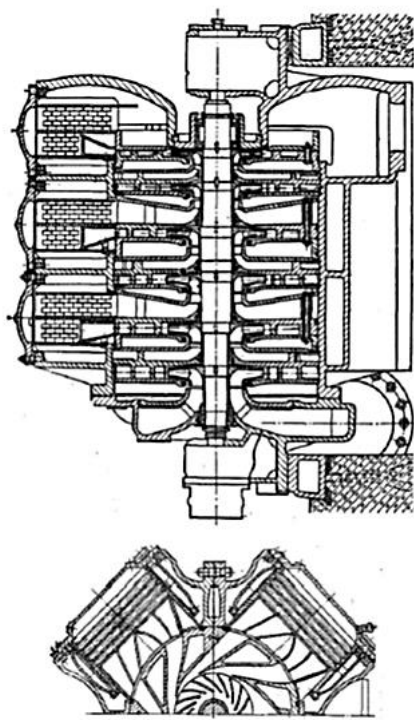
Компрессор К-100-61-2 з вбудованими охолоджувачами
